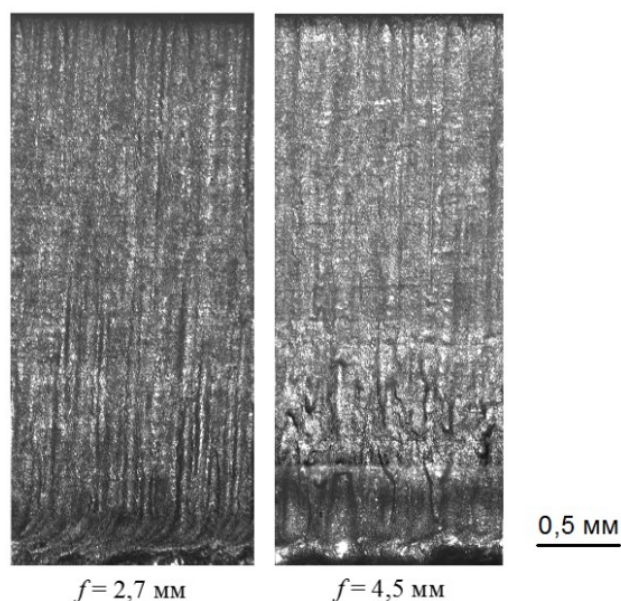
Внешний вид резов образцов стали марки Р6М5, полученных при разных положениях фокальной точки f от верхней поверхности заготовки
